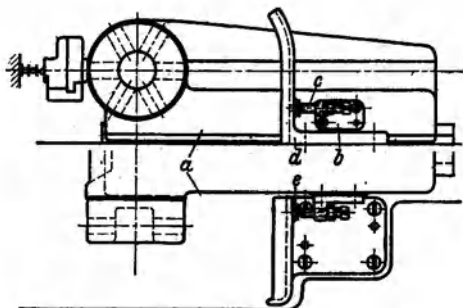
Anschlag für den Revolverschlitten. An dem Revolverschlitten *a* ist der Anschlagbock *b* befestigt, der die einstellbare Anschlagschraube *c* trägt. Als Gegenanschlag dient der am Maschinenbett befestigte Spritzwinkel *d* mit dem Anschlagbolzen *e*. Bedingung ist, daß beim Anschlagen die Kurve ihren höchsten Punkt erreicht und alle anderen Werkzeuge bei ihren vorderen Endstellungen größere Abstände des Revolverkopfes von der Spindel haben.
